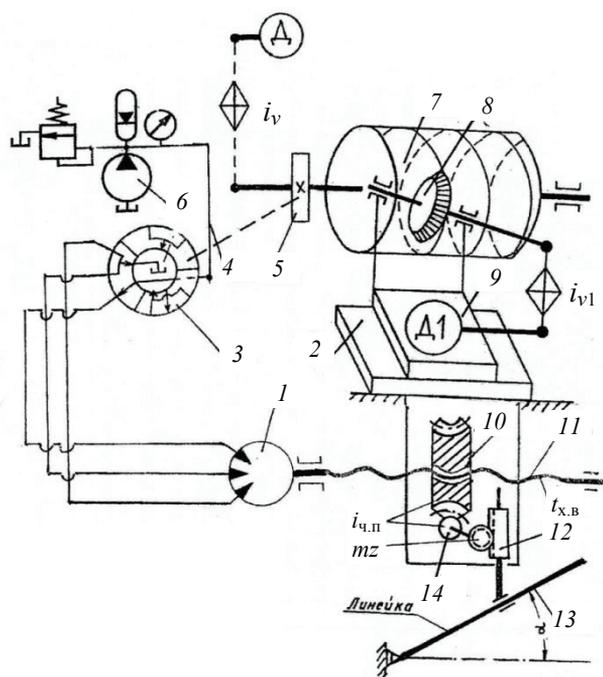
Структурная схема станка резьбофрезерного с гидравлическими формообразующими связями для нарезания цилиндрических винтовых поверхностей переменного шага с модифицированным механизмом приращения шага
